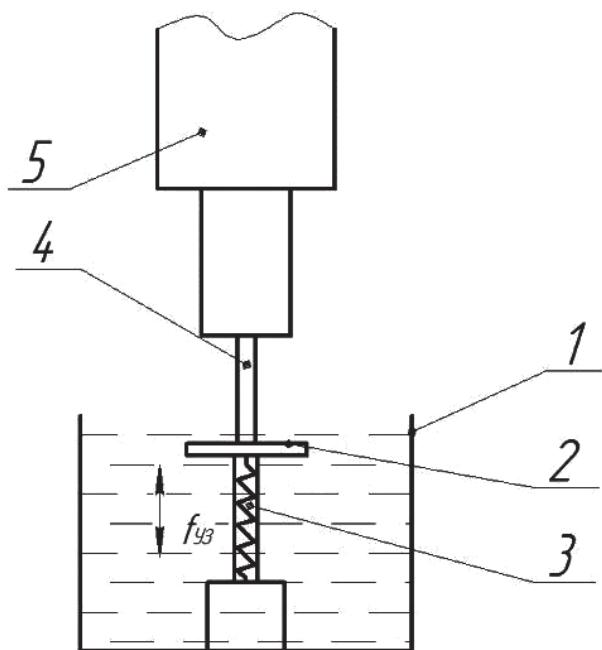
Схема наложения УЗК на обрабатываемую деталь
